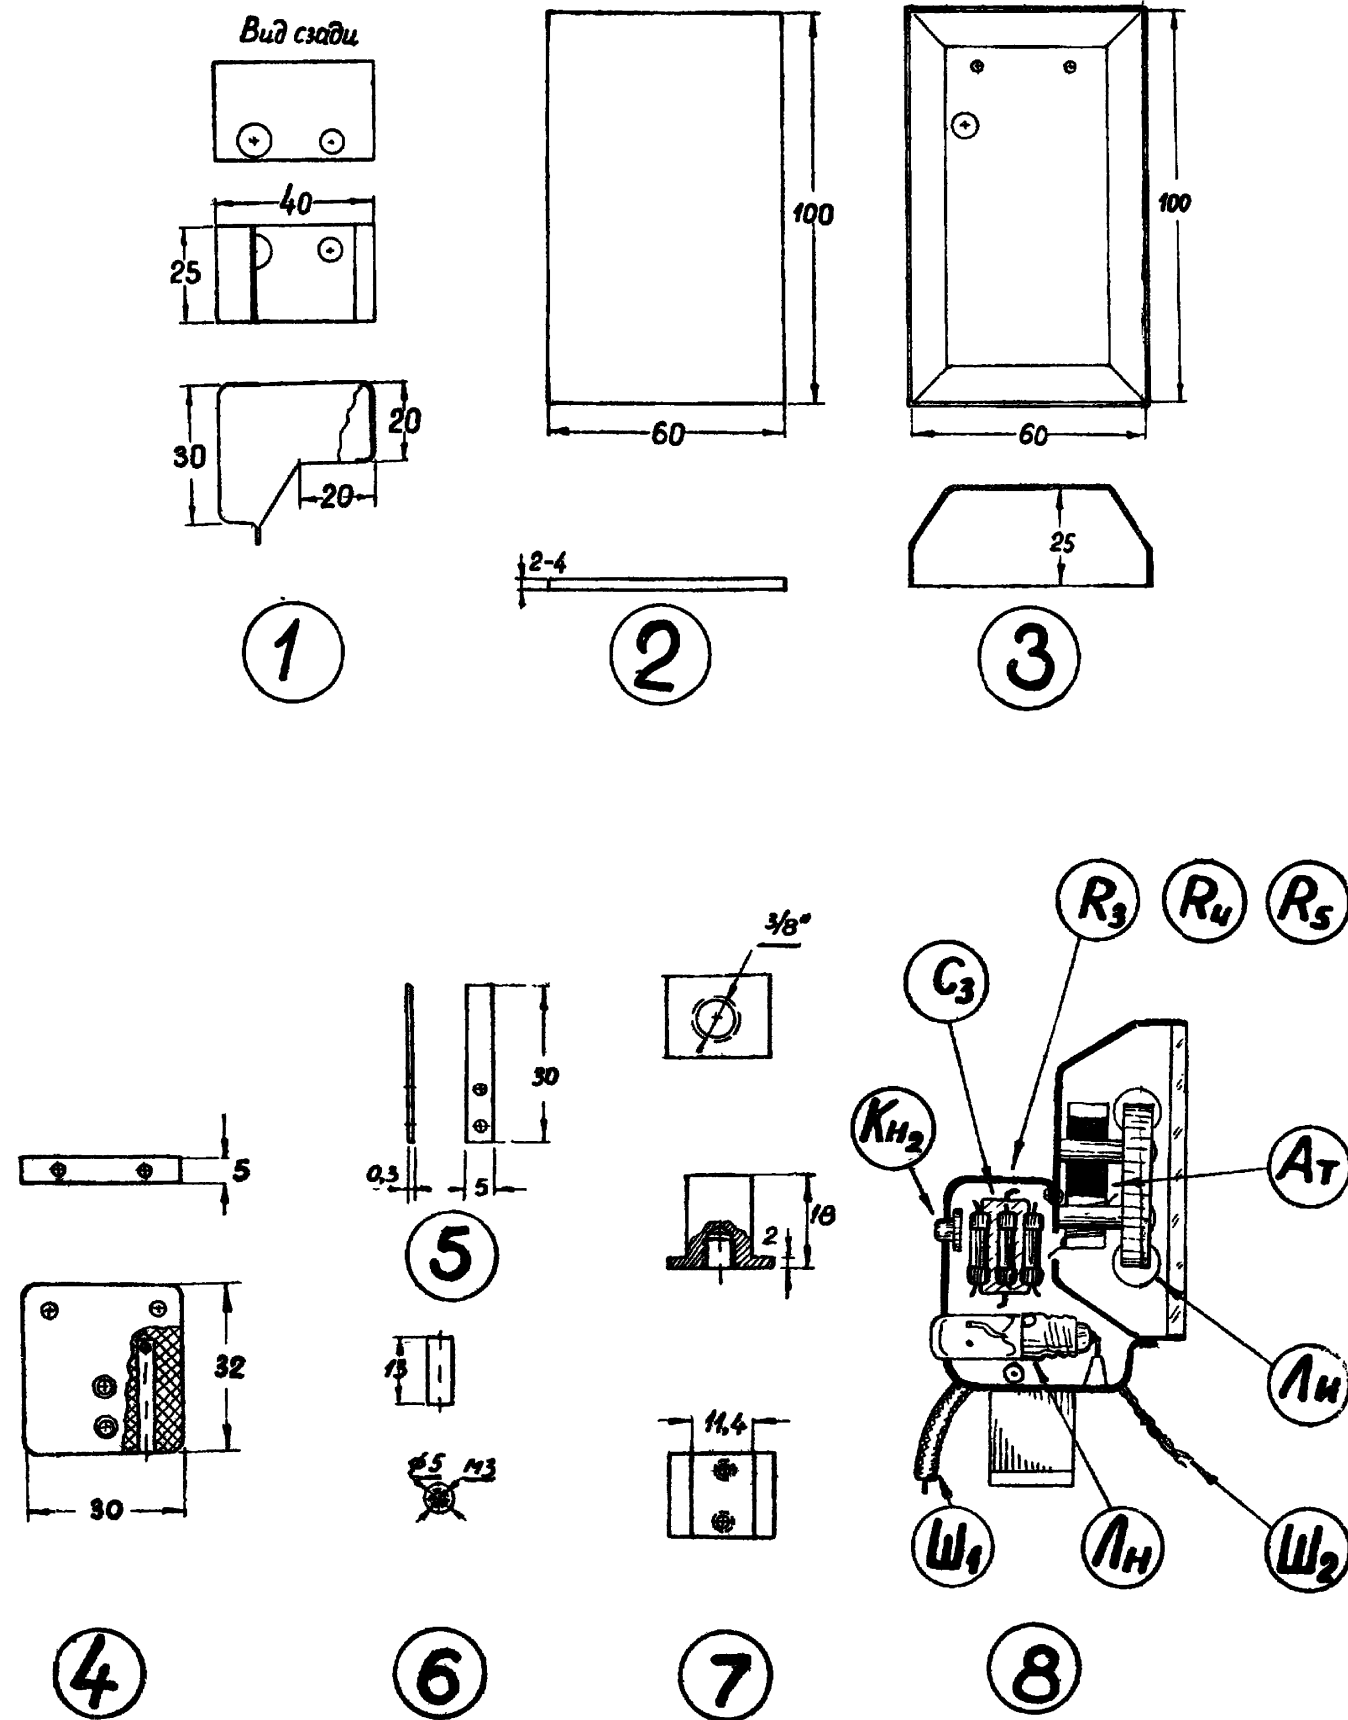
Детали 1—7 и компоновка 8 рефлектора
